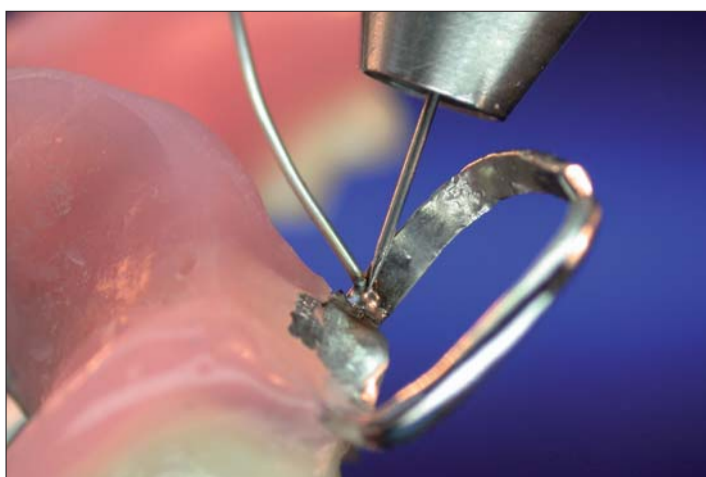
Es ist zwingend notwendig, auch die Innenseite der Klammer zu verschweißen.
